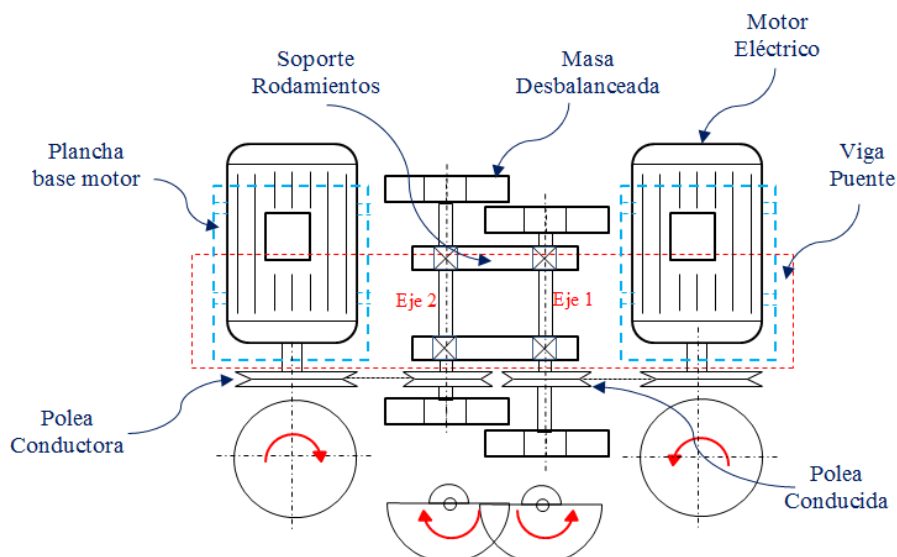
Disposición del sistema de excitación en la viga puente.
